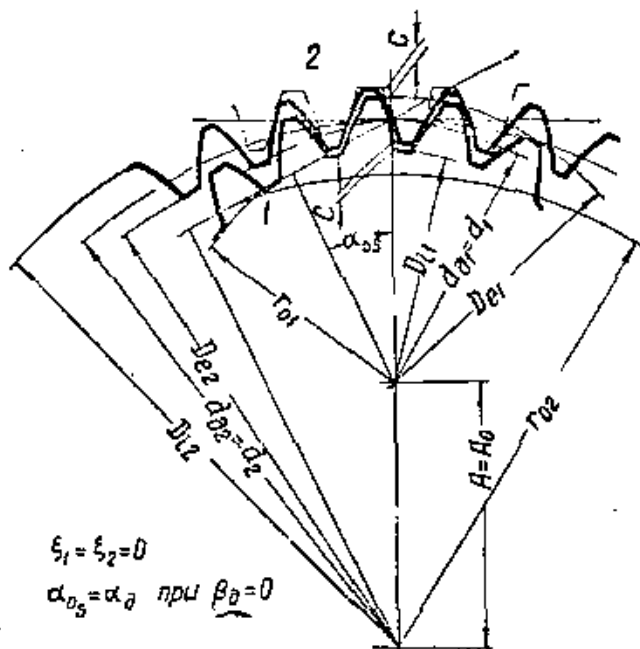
Цилиндрические зубчатые колеса внутреннего зацепления.
